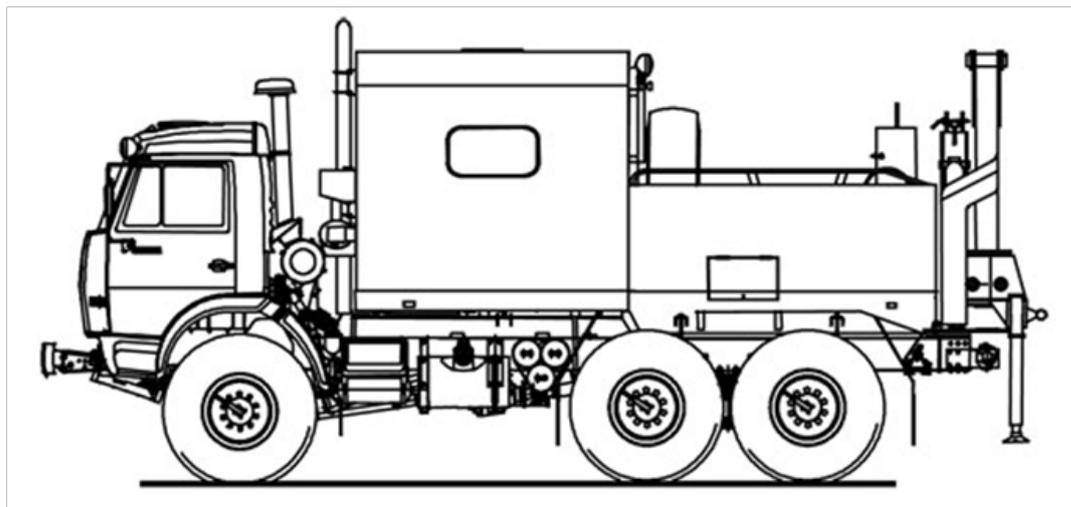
Агрегат для ремонта и обслуживания станков-качалок на шасси 6×6 Камаз 43118
